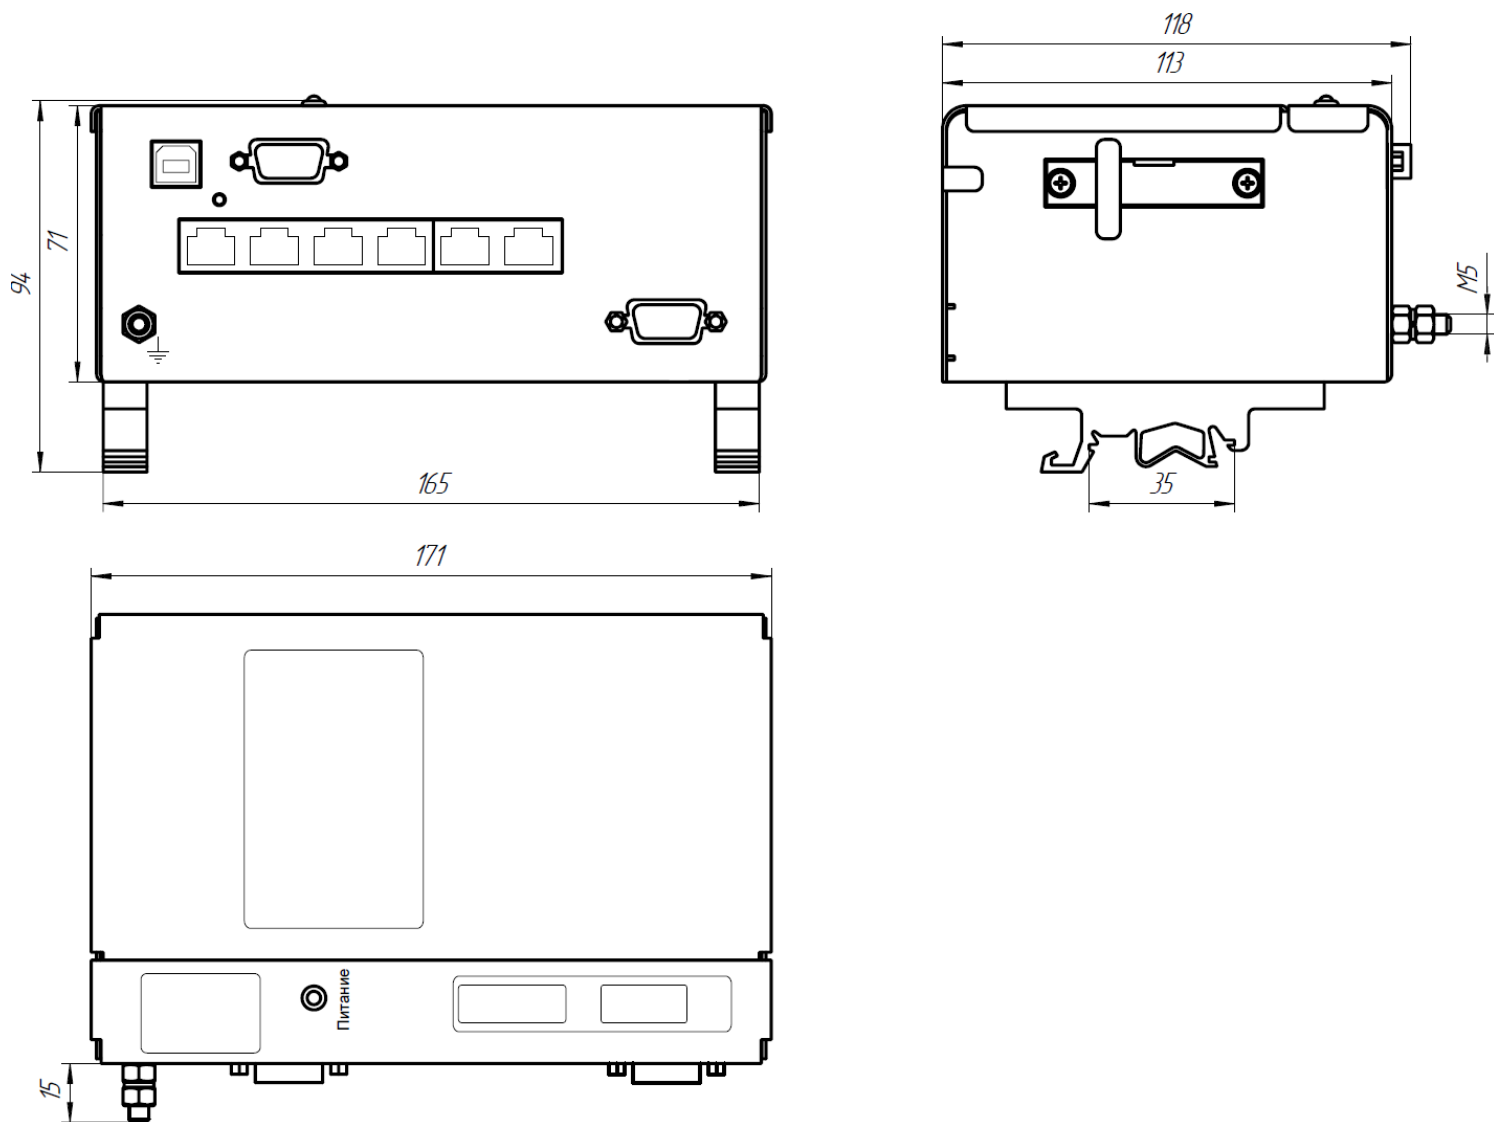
Внешний вид и габаритные размеры контроллера вагона
